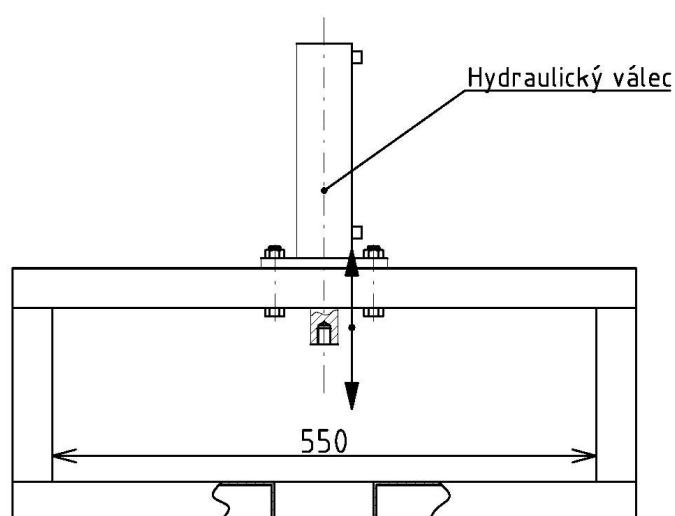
Varianta č. 1, ustavení pro vytahování
